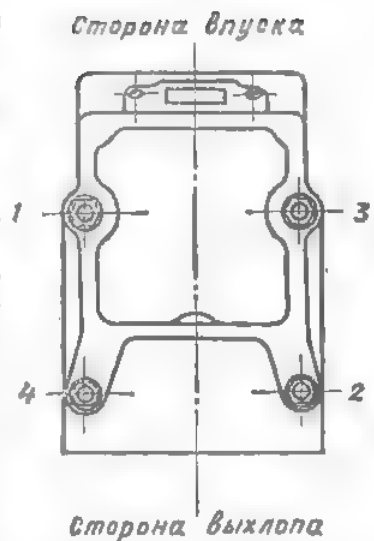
Порядок затяжки болтов крепления головки цилиндров
